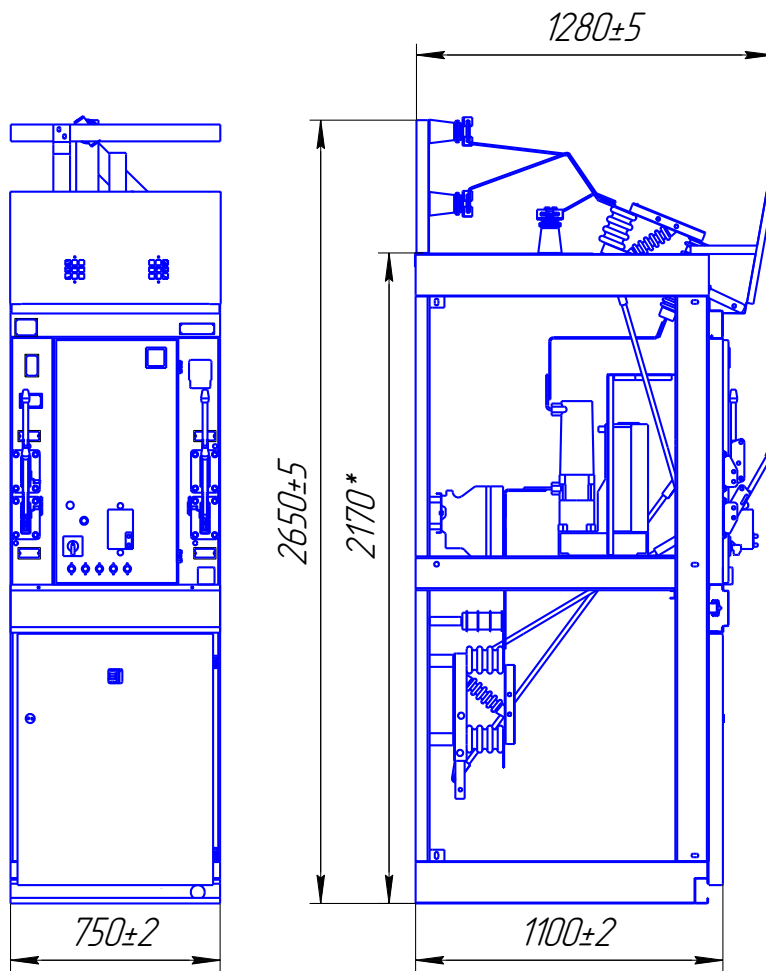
Габаритные размеры камеры КСО - 203 - 02.1
